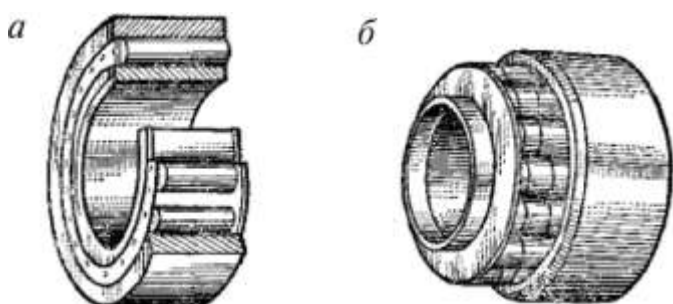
Роликовые подшипники с длинными цилиндрическими (а) и витыми (б) роликами
